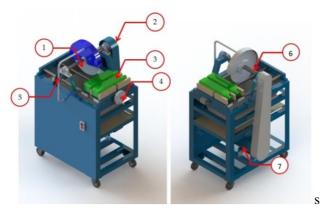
Mesin pemotong botol kaca silinder posisi horizontal
